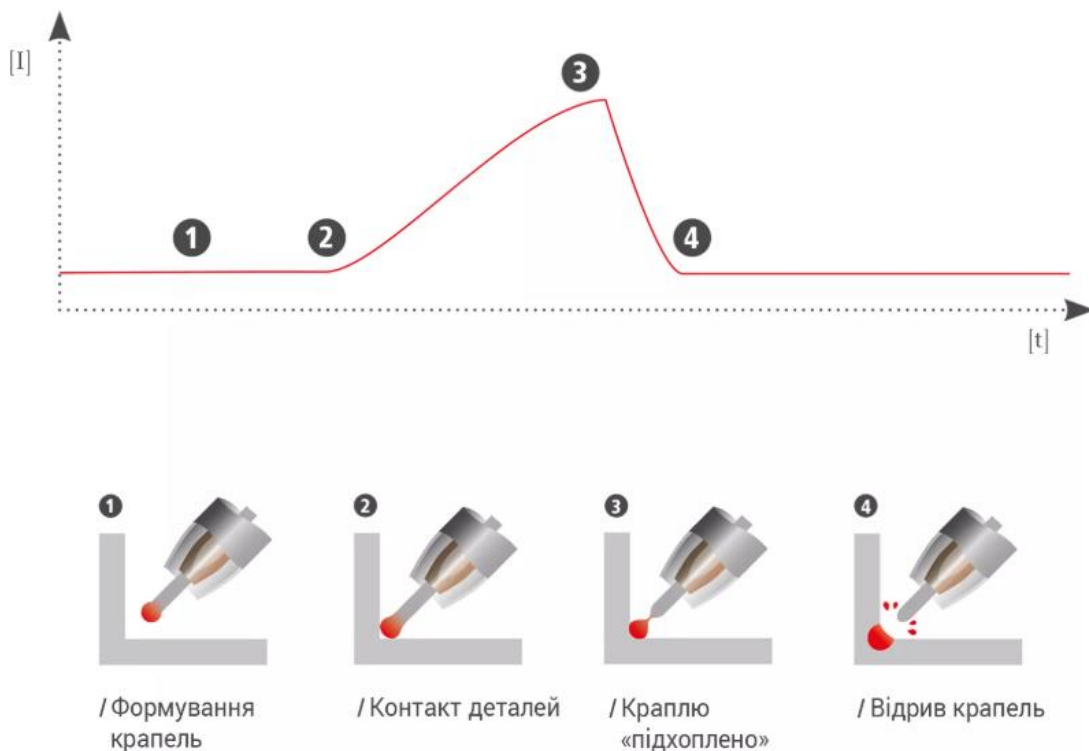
Характеристика процесу MIG/MAG зварювання короткою дугою
